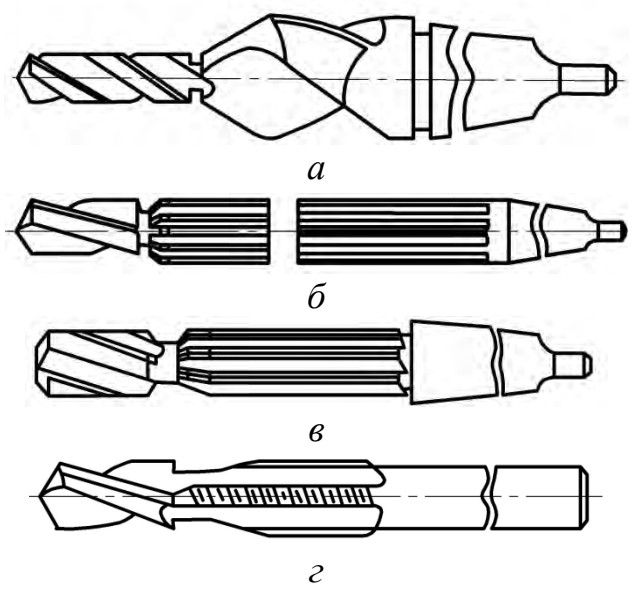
Комбинации различных режущих инструментов: а — сверло-зенковка; б — сверло-развертка; в — зенкер-развертка; г — сверло-метчик
